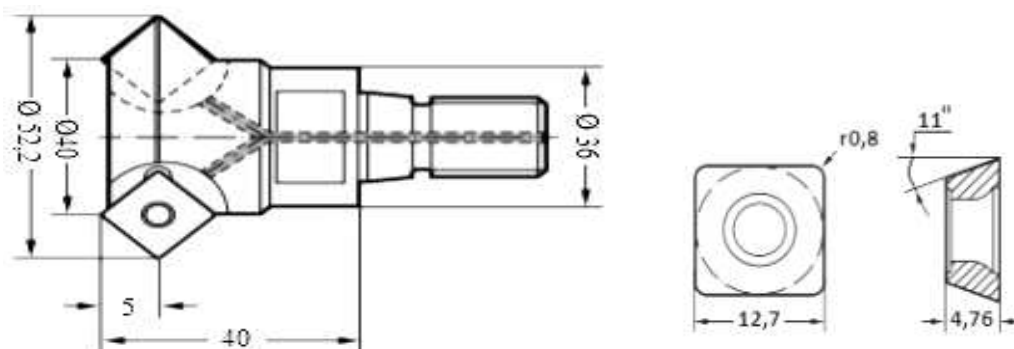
фреза F2232.T36.040.Z04.05, пластина SPMT120408D51WSP45
